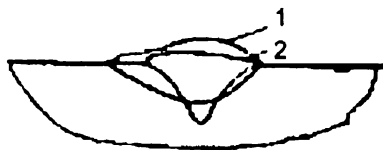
Схема форм проплавления металла при сварке в среде инертных газов:
